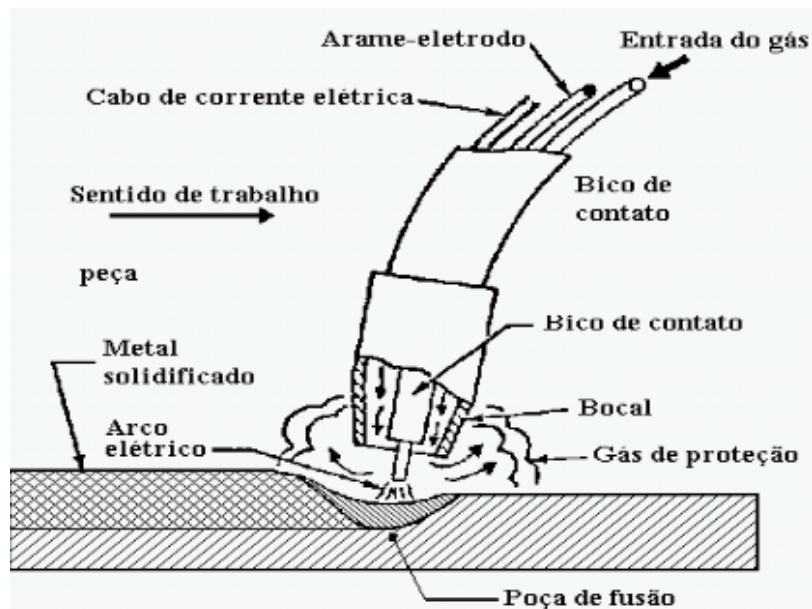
Componentes e princípios de funcionamento da soldadura MIG/MAG [29].
